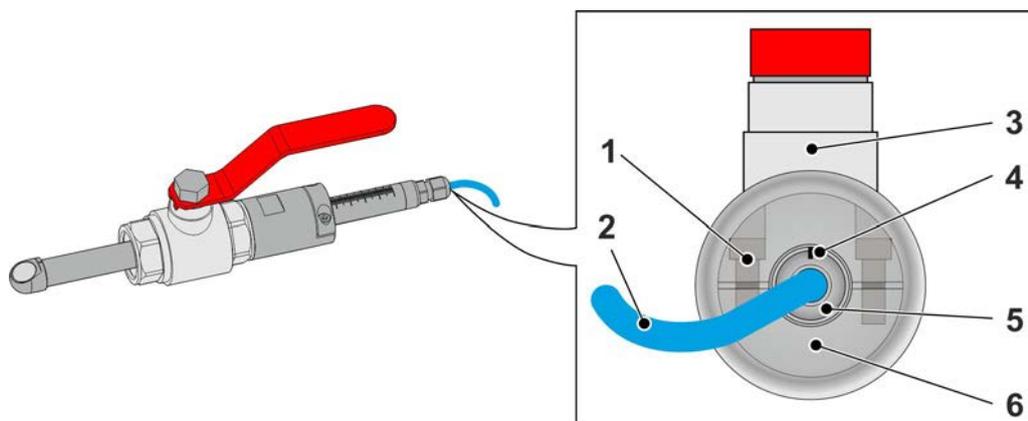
Rohrsensor CSM mit Anschweißstutzen
